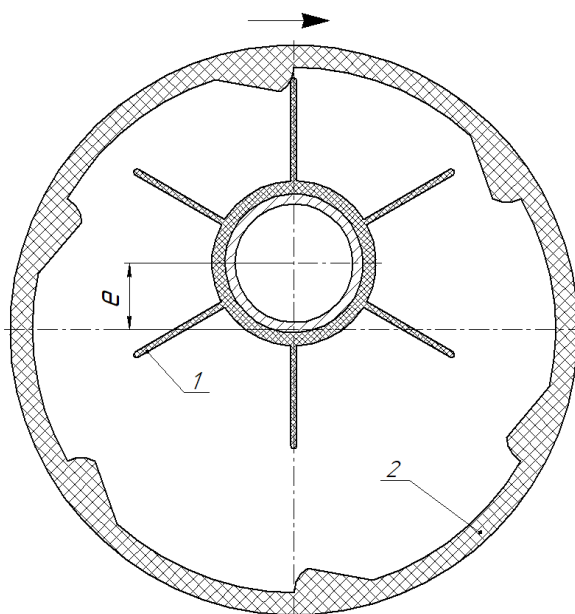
Основные детали ЖВН с кинематическим замыканием, изготовленные из СВМПЭ: 1 – рабочее колесо, 2 – корпус.
